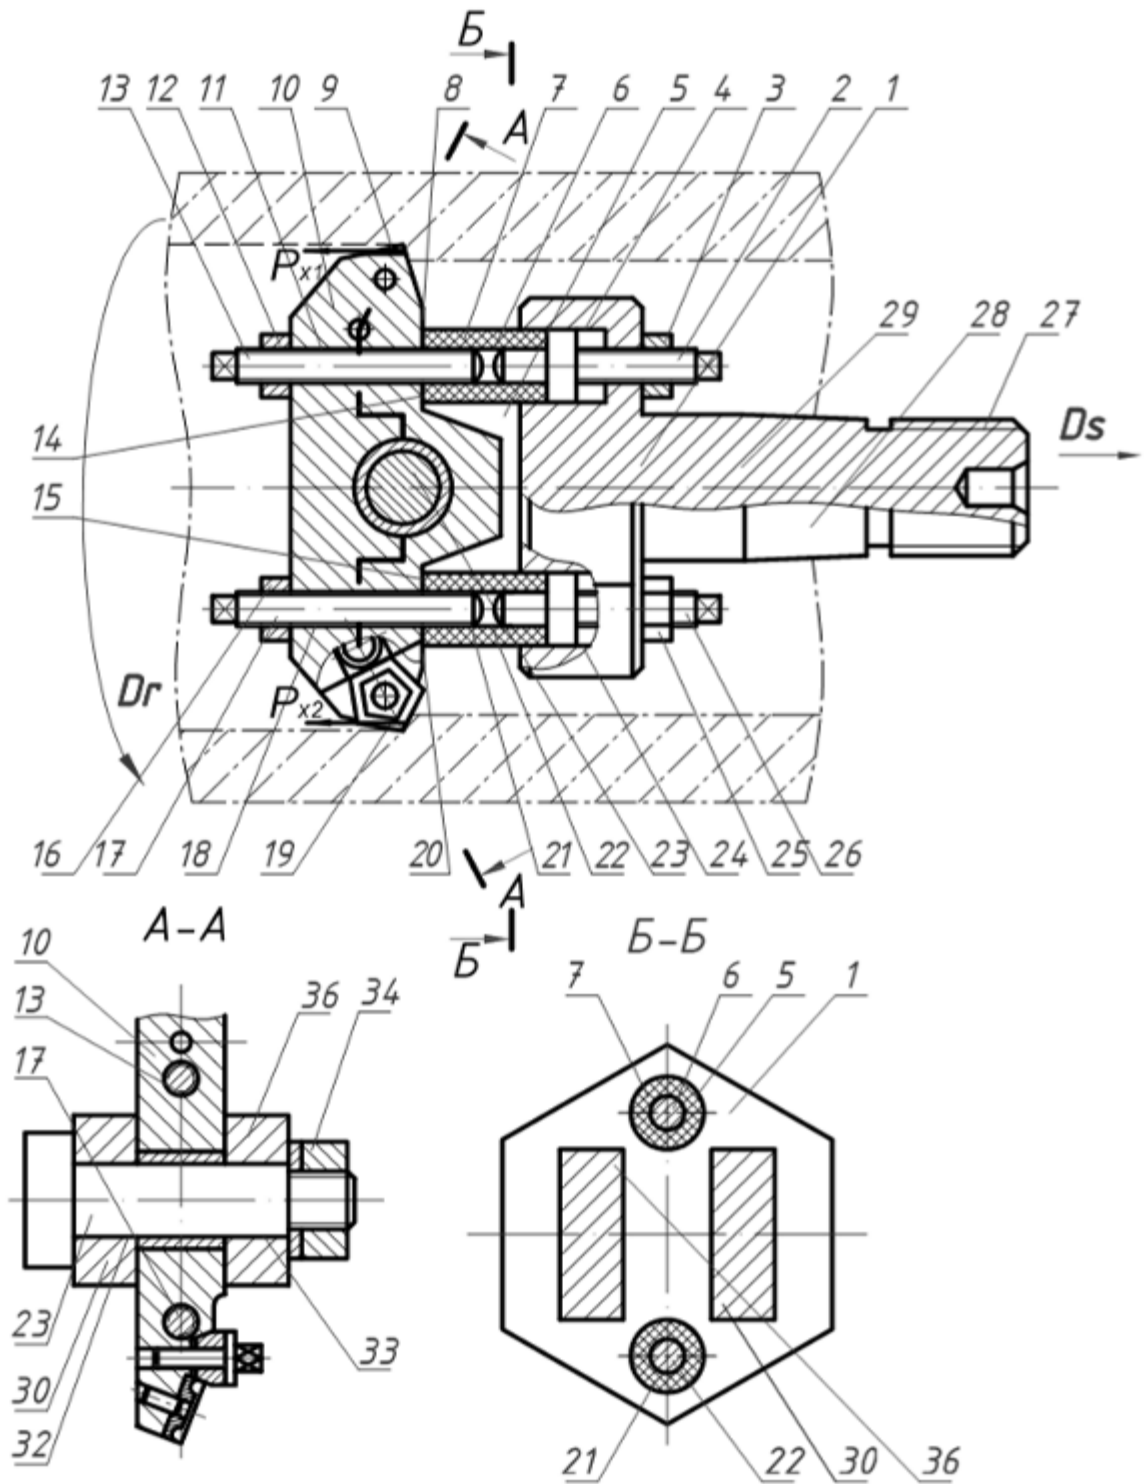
Конструкція прогресивної дворізцевої адаптивної розточувальної головки [129]
